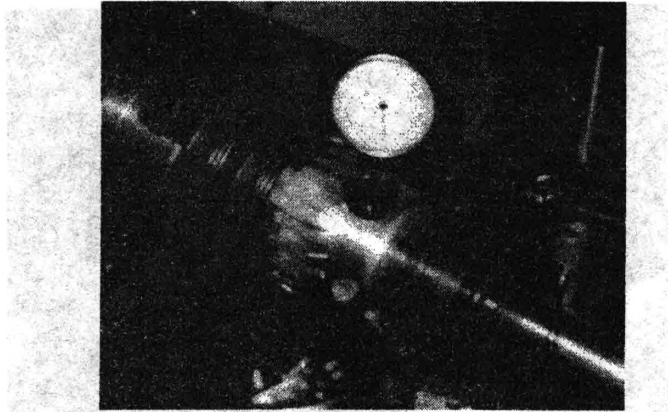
Вимірювання обвідної обробленої поверхні заготовки з однаковими виступами, відстань між якими є випадковою величиною
